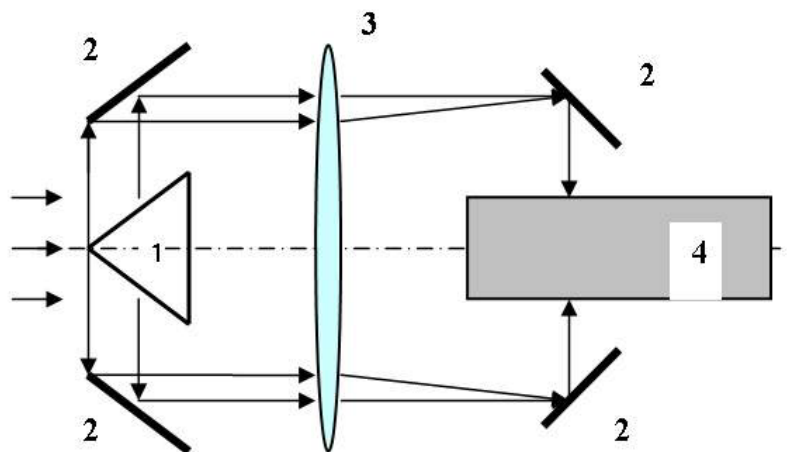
Оптическая схема фокусировки излучения на цилиндрическую деталь:
